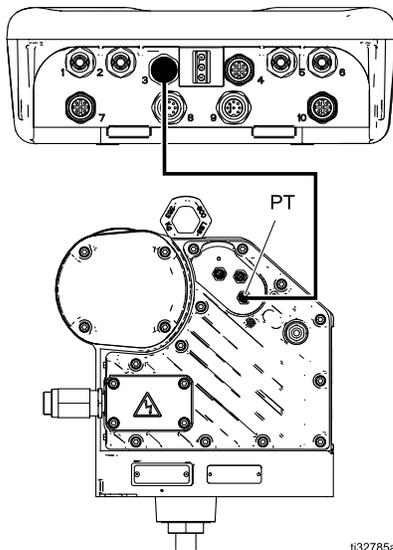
Pumpensteuermodul-Anschlüsse an der E-Flo DC Pumpe, einphasig
